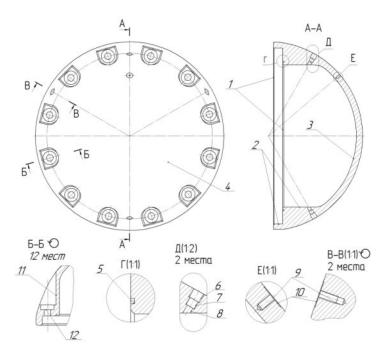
Эскиз детали «Крышка ступицы гребного винта» с обозначением обрабатываемых поверхностей
